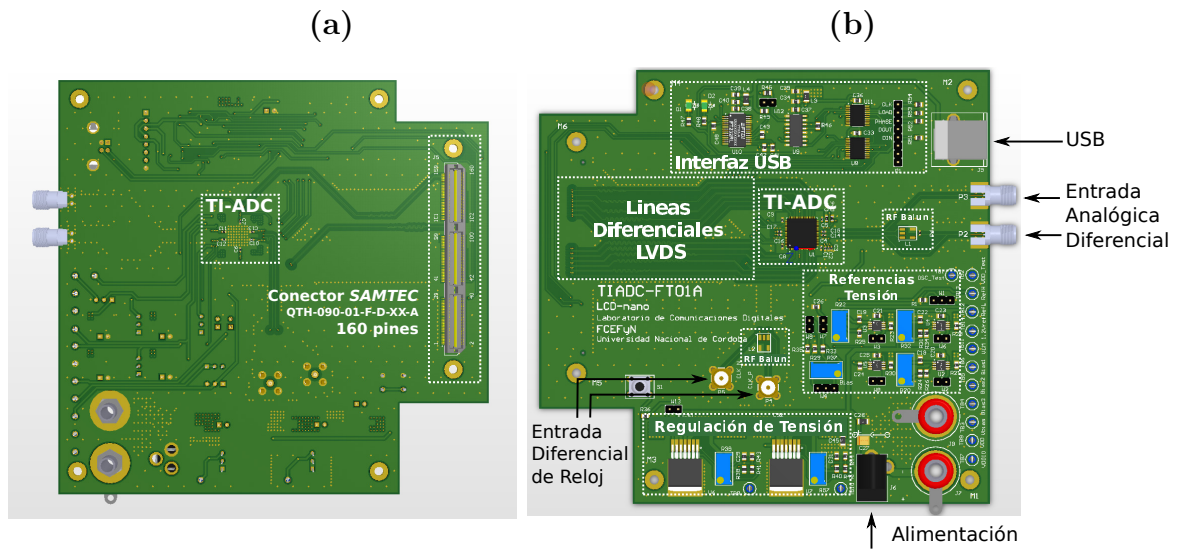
Diseño del PCB de soporte para el chip conversor: (a) vista de reverso de la placa con conector a FPGA, (b) vista superior de la placa con montaje de componentes principales.
